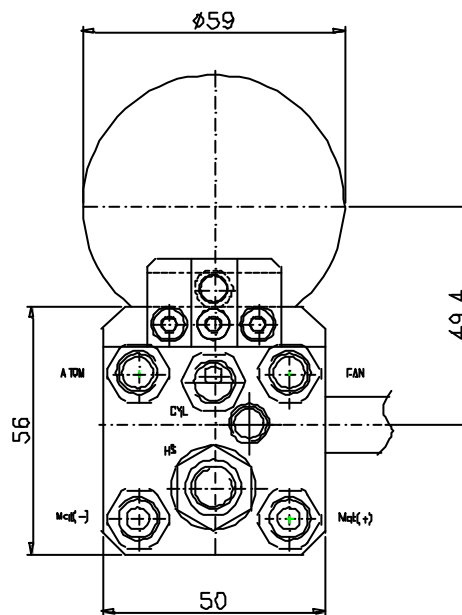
Rückansicht des Adapters AEMD 4500 mit Schlauchbelegung
